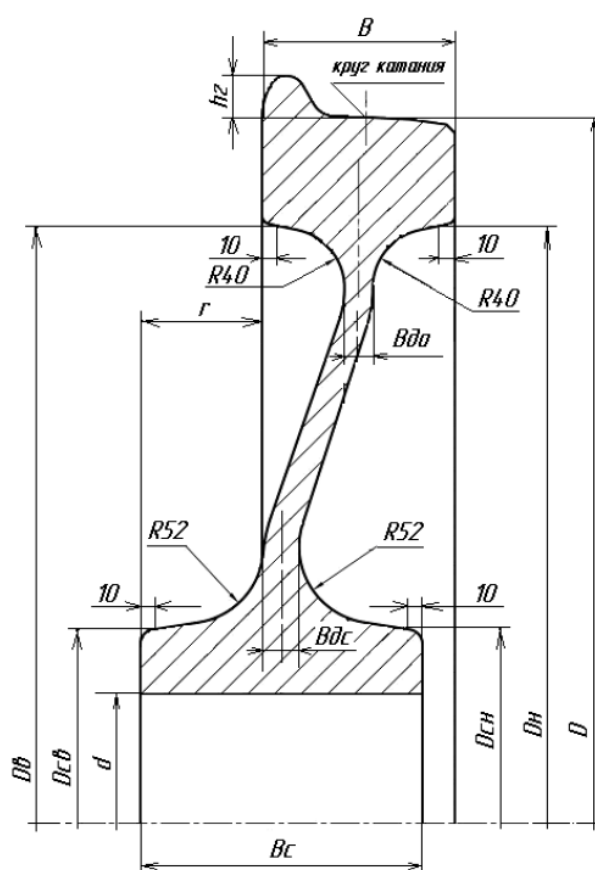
Конструкція колеса цільнокатаного з плоскоконічним диском
